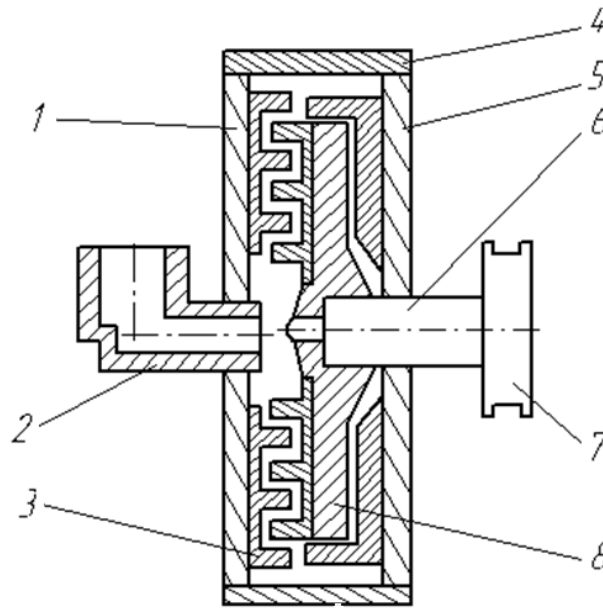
Принципова схема колоїдного млина [30, 74]: 1 – статор, 2 – трубопровід для підведення сировини, 3 – зубці стаціонарні, 4 – корпус, 5 – кришка, 6 – вал, 7 – шків, 8 – робоче колесо із зубцями
